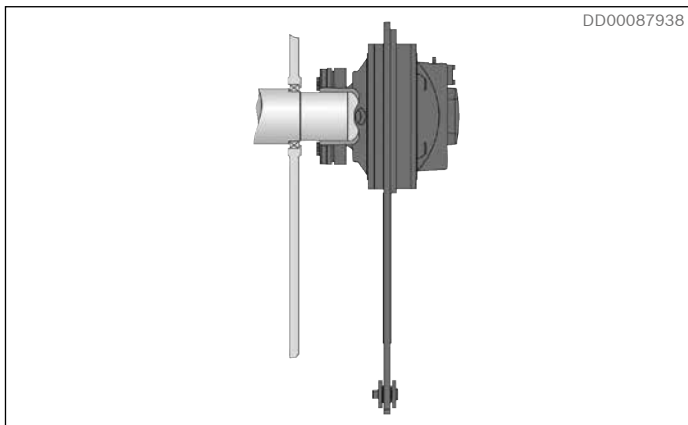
Motormontage der Drehmomentstütze mit Schrumpfscheibe.
